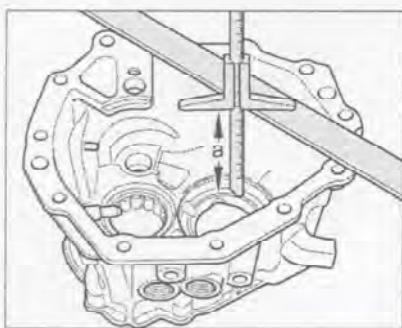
Измерьте расстояние a на новом и старом корпусах подшипников.
